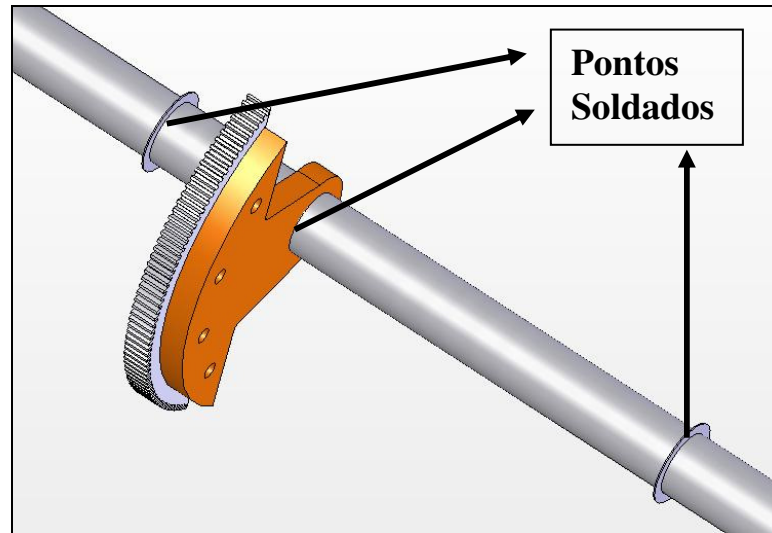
Pontos que serão fixados por solda a toda volta.
